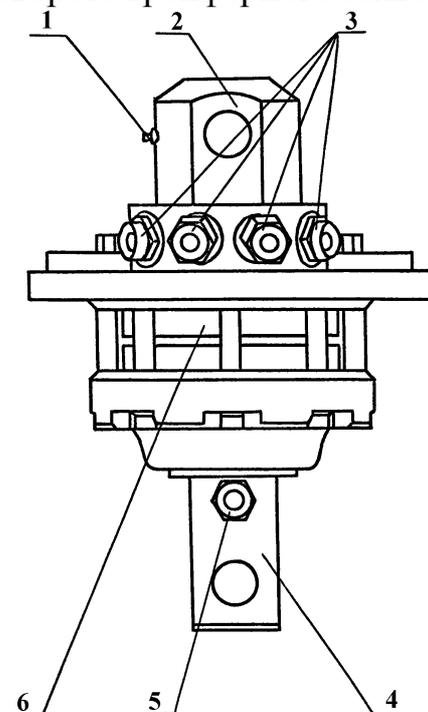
Ротатор: 1 – масленка; 2 – серьга; 3, 5 – штуцеры; 4 – вал; 6 – гидромотор
